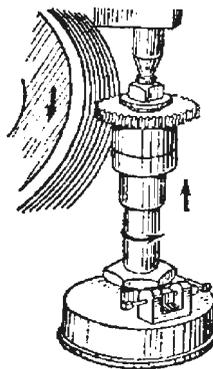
Зубошлифование цилиндрического зубчатого колеса червячным шлифовальным кругом
